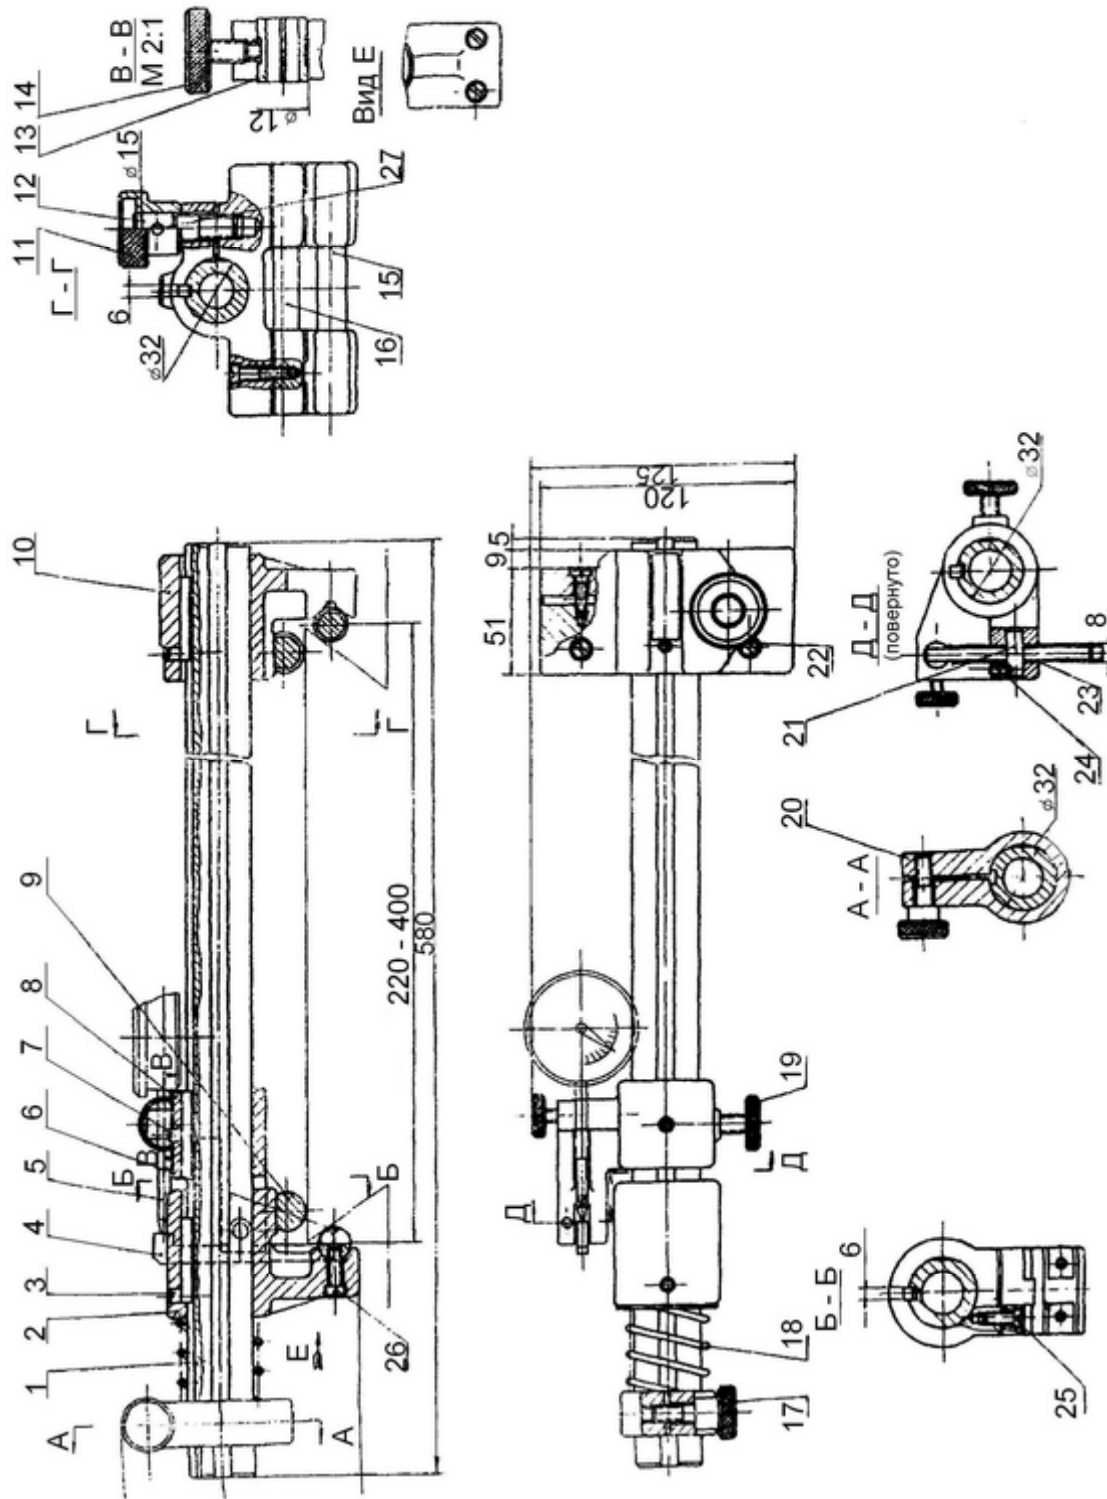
Приспособление для проверки направляющих типа «ласточкин хвост» СД 8532 – 4010
